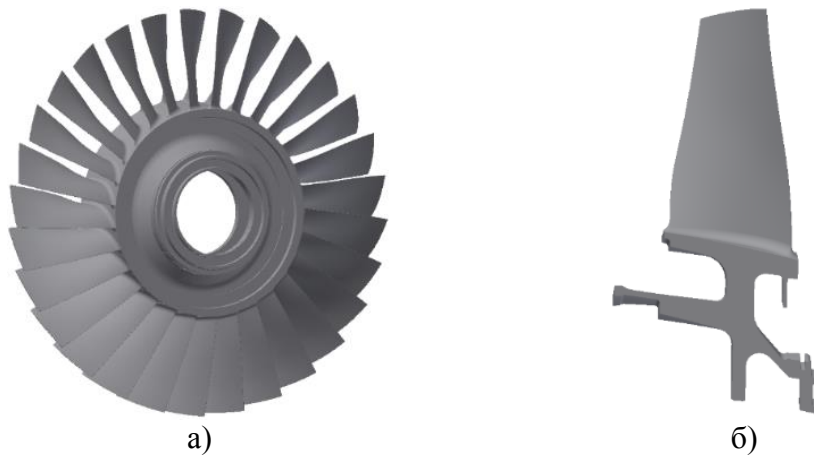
Рабочее колесо фирмы Rolls-Royce (а - колесо в сборе;
